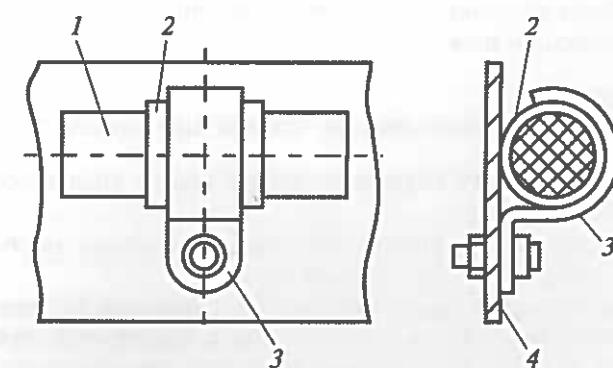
Крепление монтажного жгута металлической скобой на шасси прибора:
